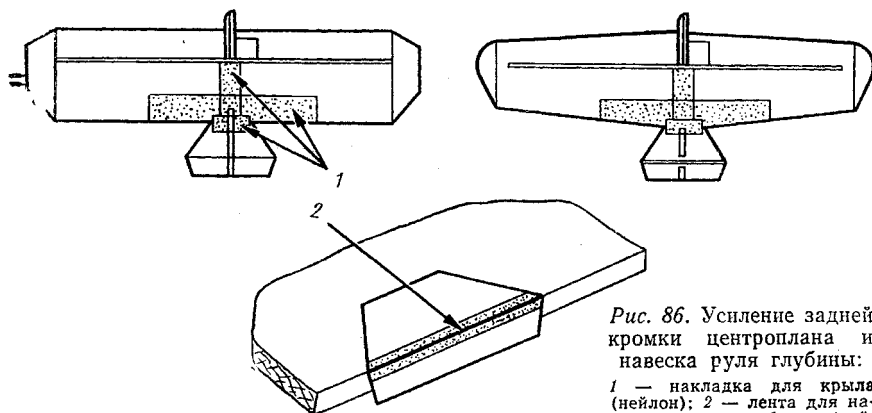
Усиление задней кромки центроплана и навеска руля глубины:
